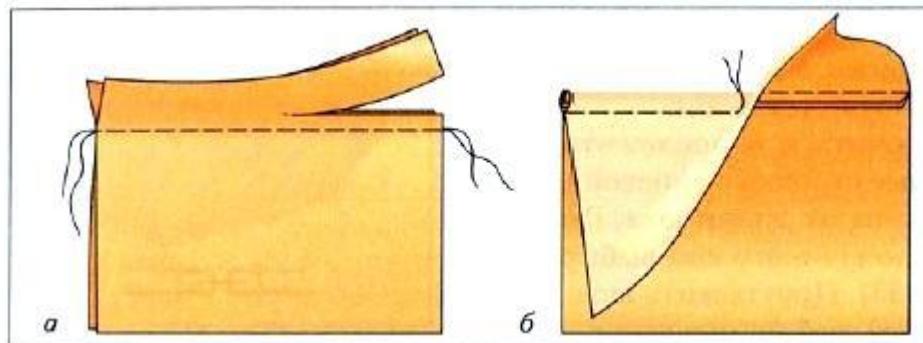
Выполнение двойного шва: а — срезание припусков; б — прокладка шва
